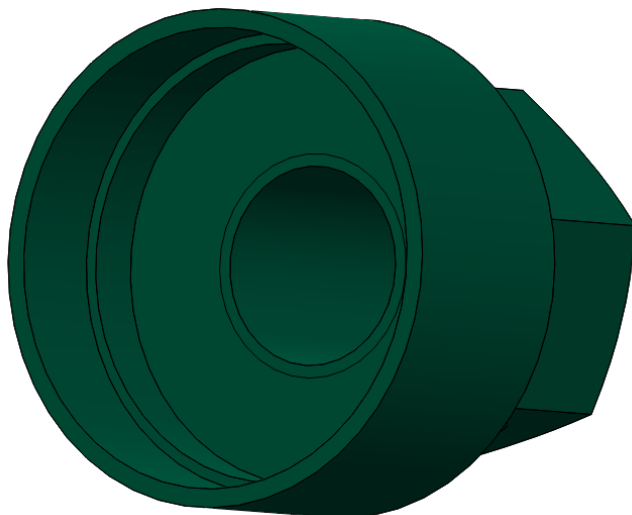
Модель детали «гайка в сборе с подшипником»
